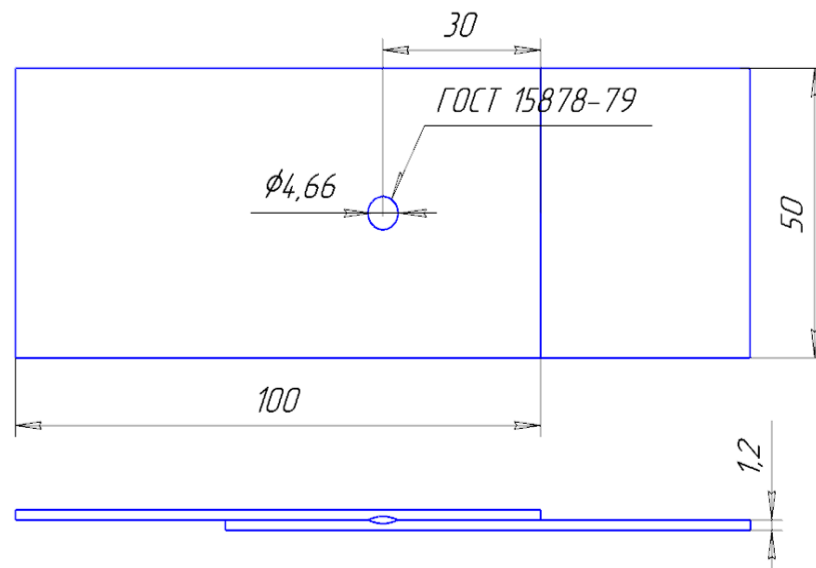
Образцы для испытаний на срез сварной точки
